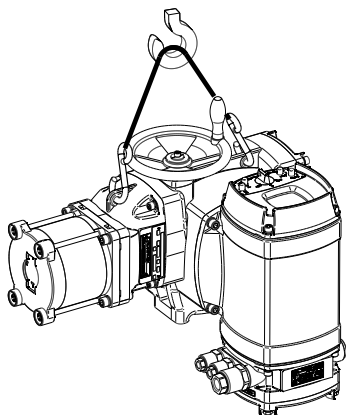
Схемы строповки механизма МЭОФ-10(К)
